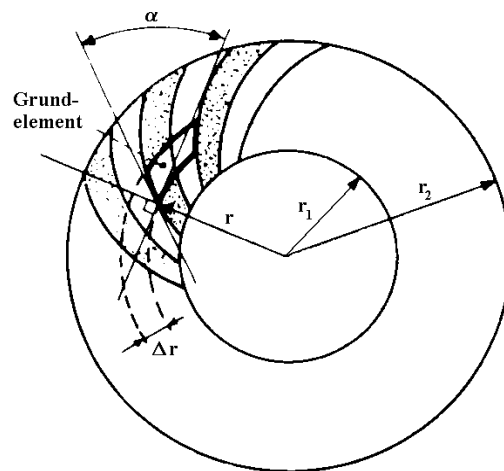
Element aus einer Lagerfläche eines Axiallagers nach MUIJDERMAN /24/
